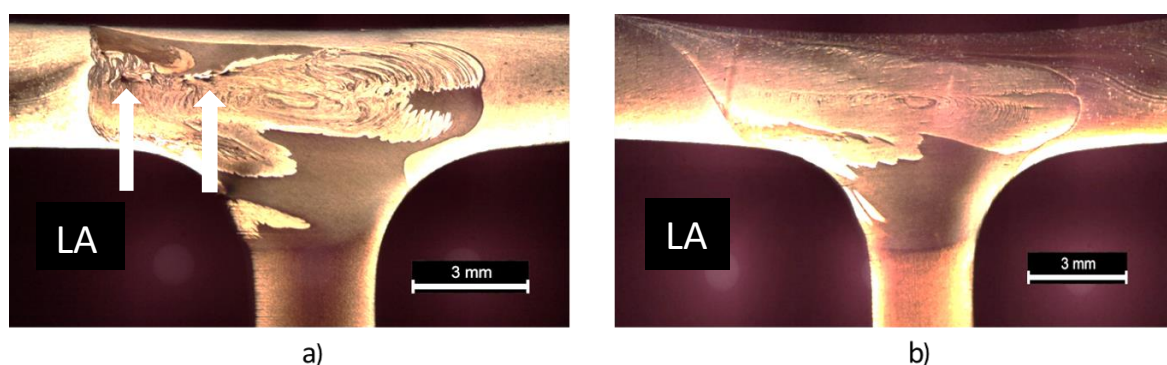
Macrografias das soldaduras: a) 562-30-M (Weck); b) 265-30-M (Weck).
